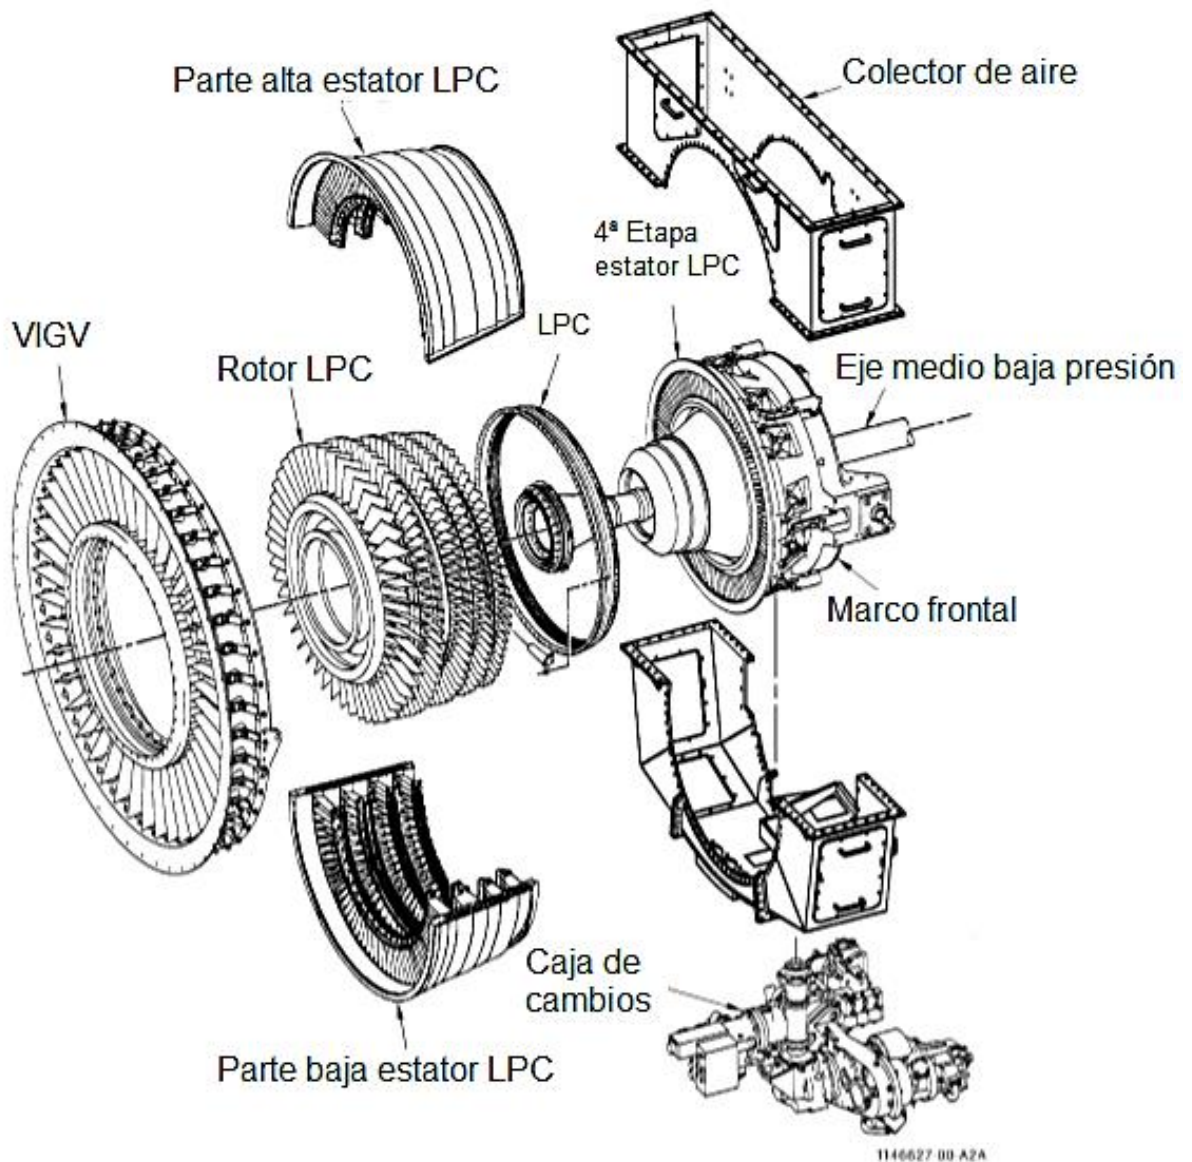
Componentes principales de la turbina de gas LM6000 PF (Hoja 1 de 3):
